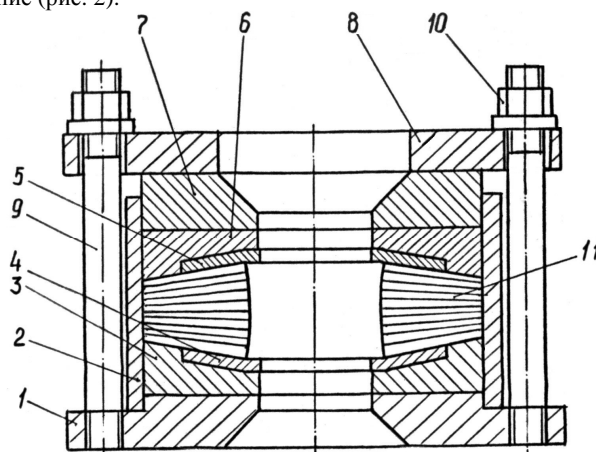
Приспособление для сборки цилиндрической иглофрезы
